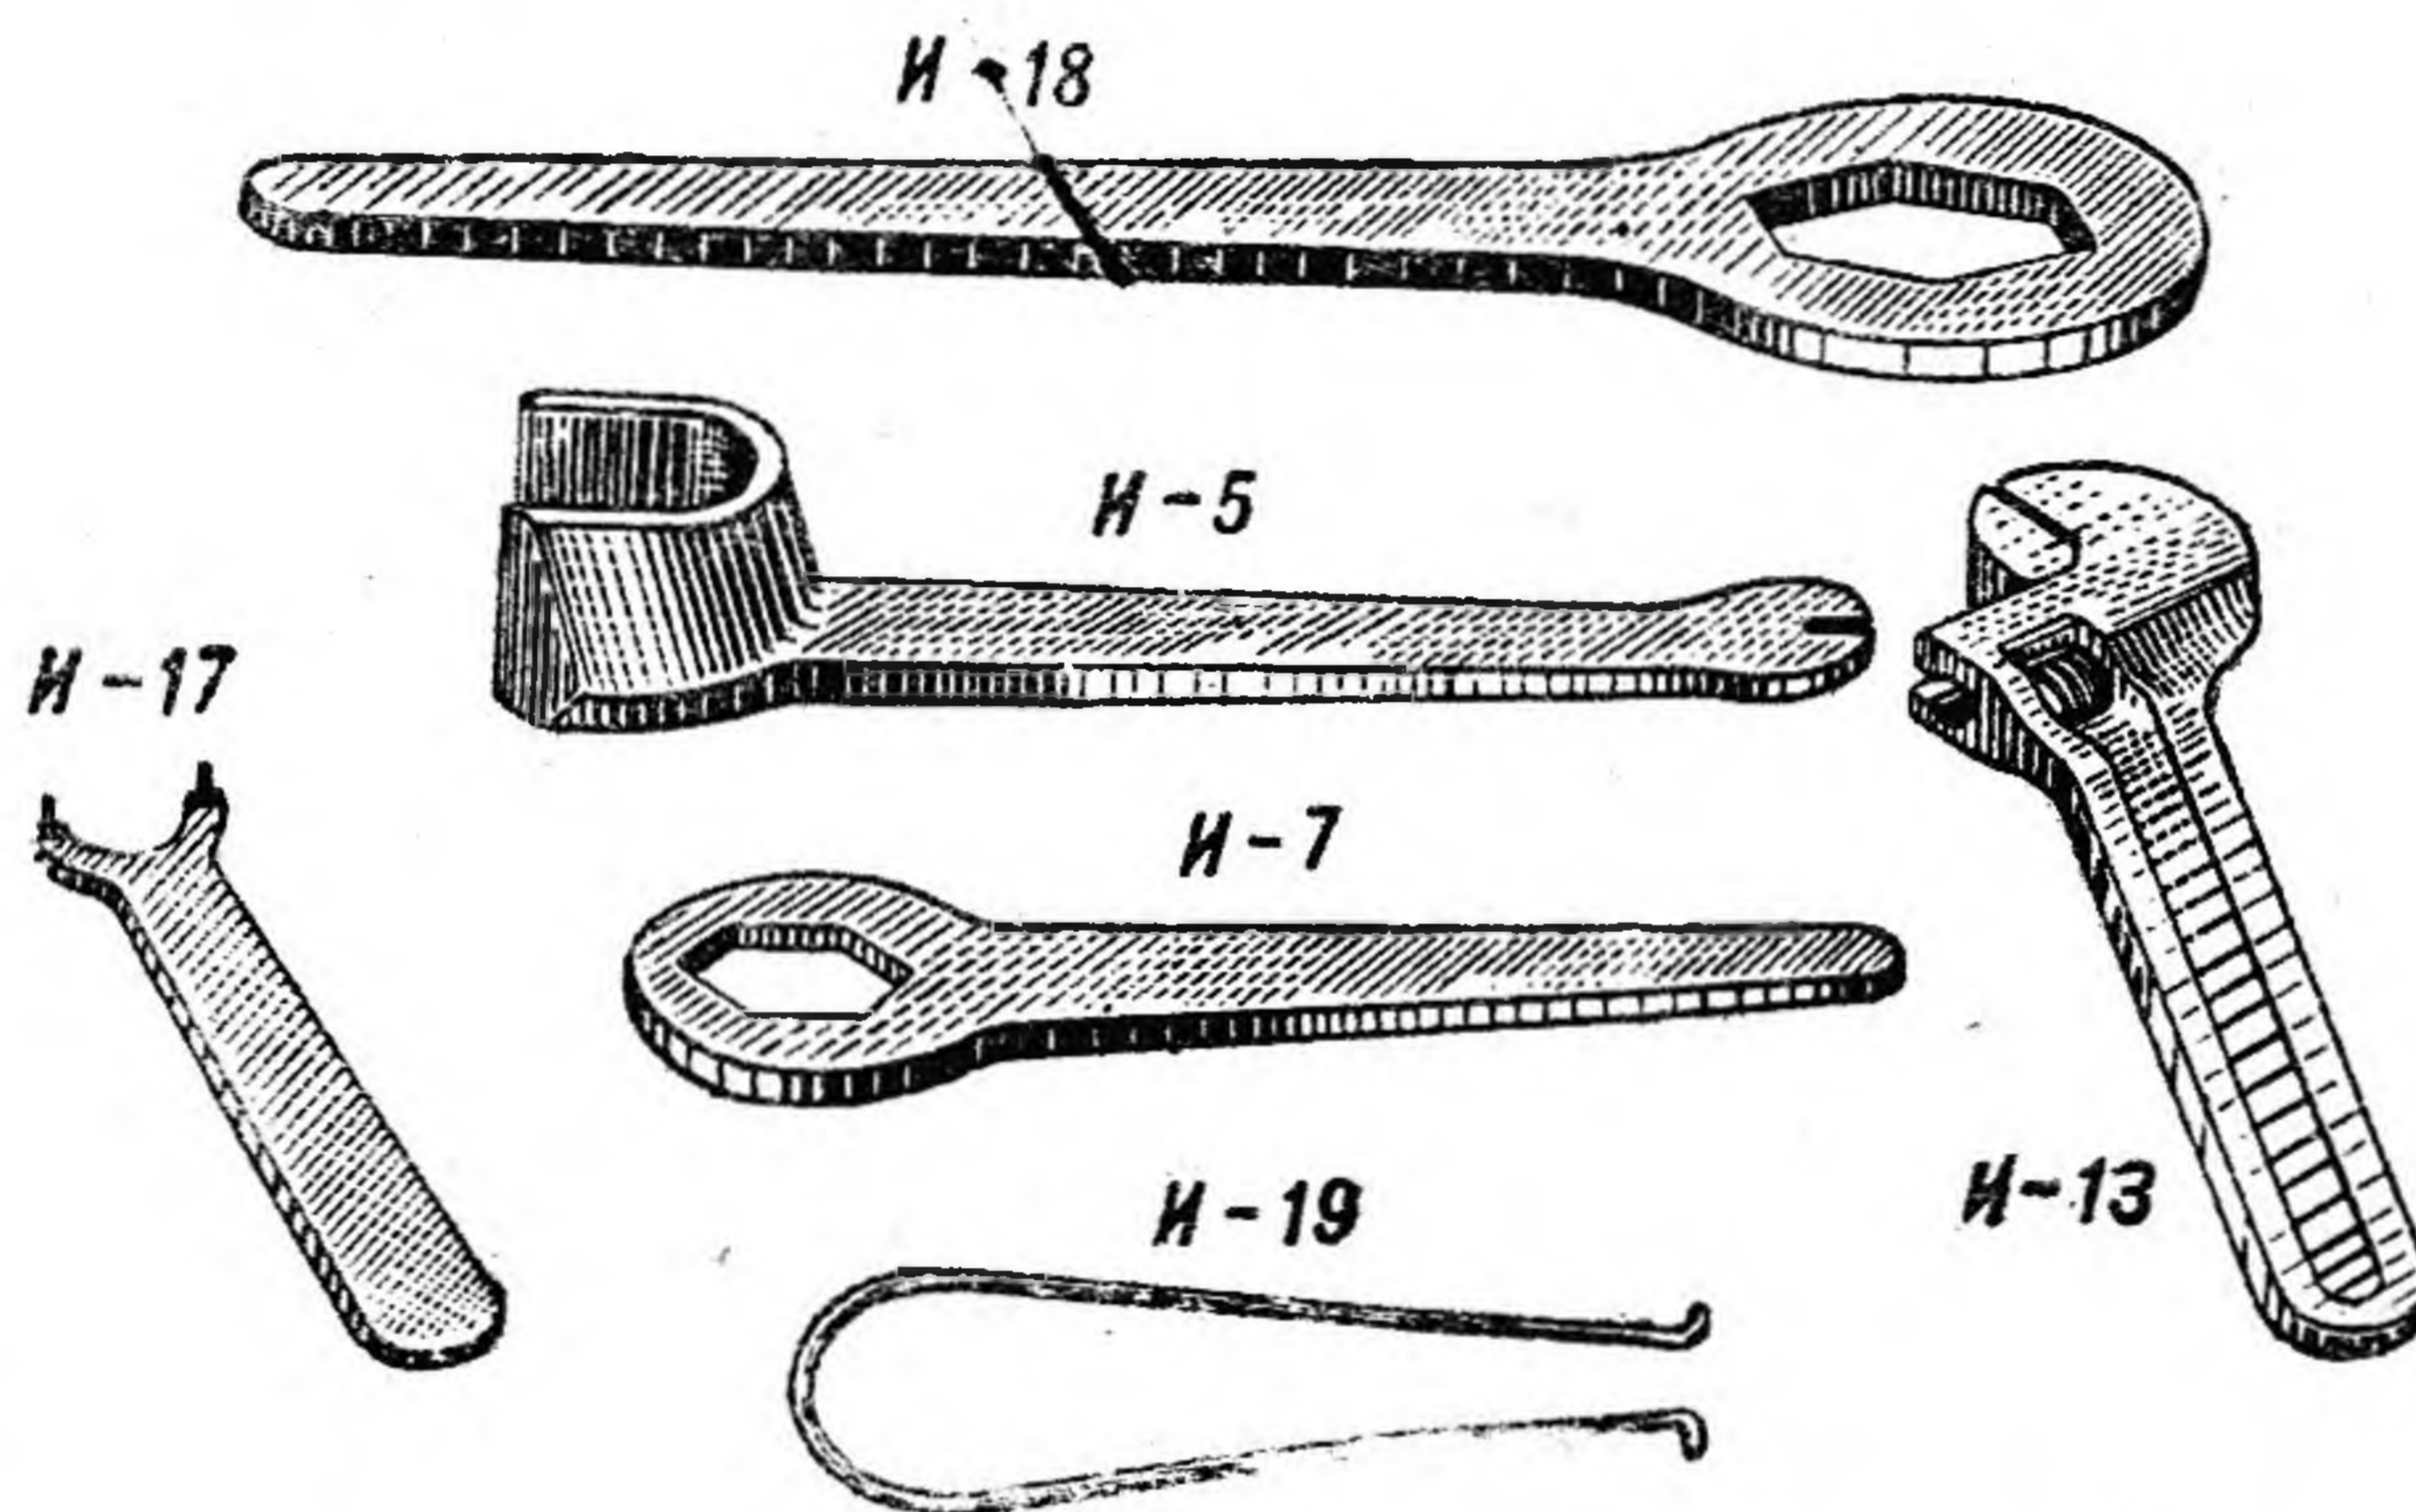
Инструмент для разборки и сборки противооткатных устройств
